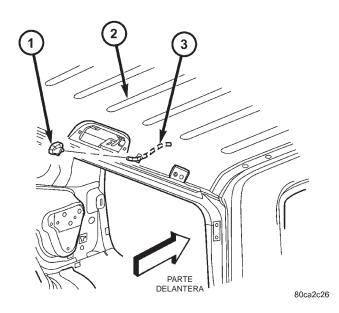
Desmontaje e instalación de boquilla del lavador trasero
